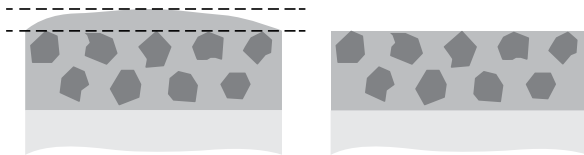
Ziel des Abrichtens: Erzeugen der Makrogeometrie
